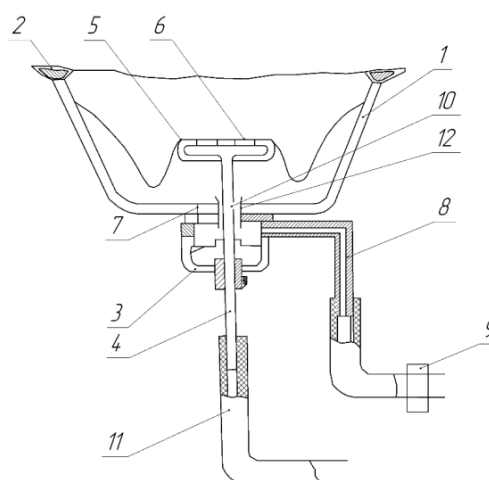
Схема устройства для массажа вымени животных двухкамерного типа: 1 – массажный колокол; 2 – уплотняющий элемент; 3 – силовая пневмокамера; 4 – шток; 5 – присосок; 6 – перфорированная крышка; 7, 10 – калиброванные отверстия; 8 – патрубок; 9 – пульсатор; 11 – шланг; 12 – направляющая
